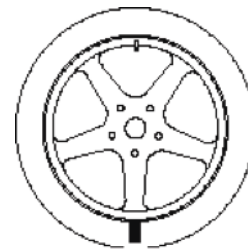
Positionnement du marquage à 180° par rapport à la valve
